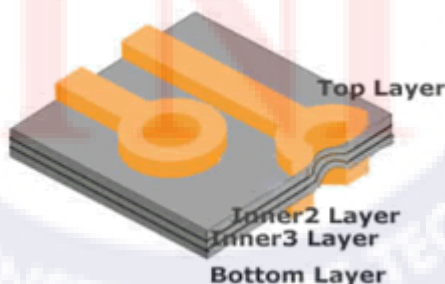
แสดงแผ่นวงจร พีซีบี (PCB) ชนิดสองหน้า (Double Side Plate through Hole)
